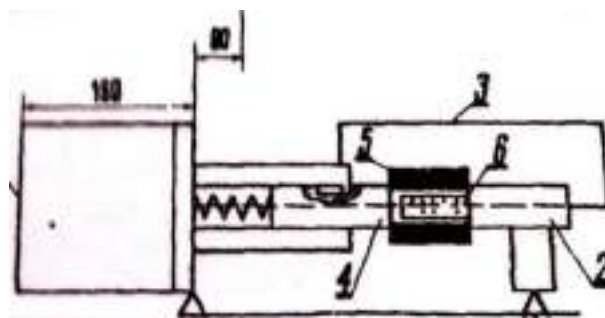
Кінематична схема устаткування гідротермічної роздачі (ГТР) поршневих пальців: 1 – пневмоциліндр; 2 – нерухомий центр; 3 – тяга гідроклапана; 4 – рухливий центр; 5 – поршневий палець; 6 – спреєр
